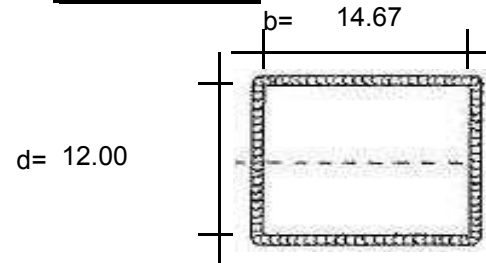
Detalle de la Soldadura en los 4 Bordes [ 13 ]
